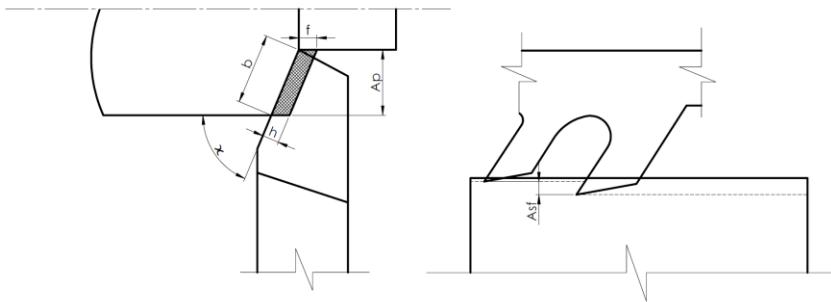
Equivalência entre largura de usinagem e penetração de avanço
